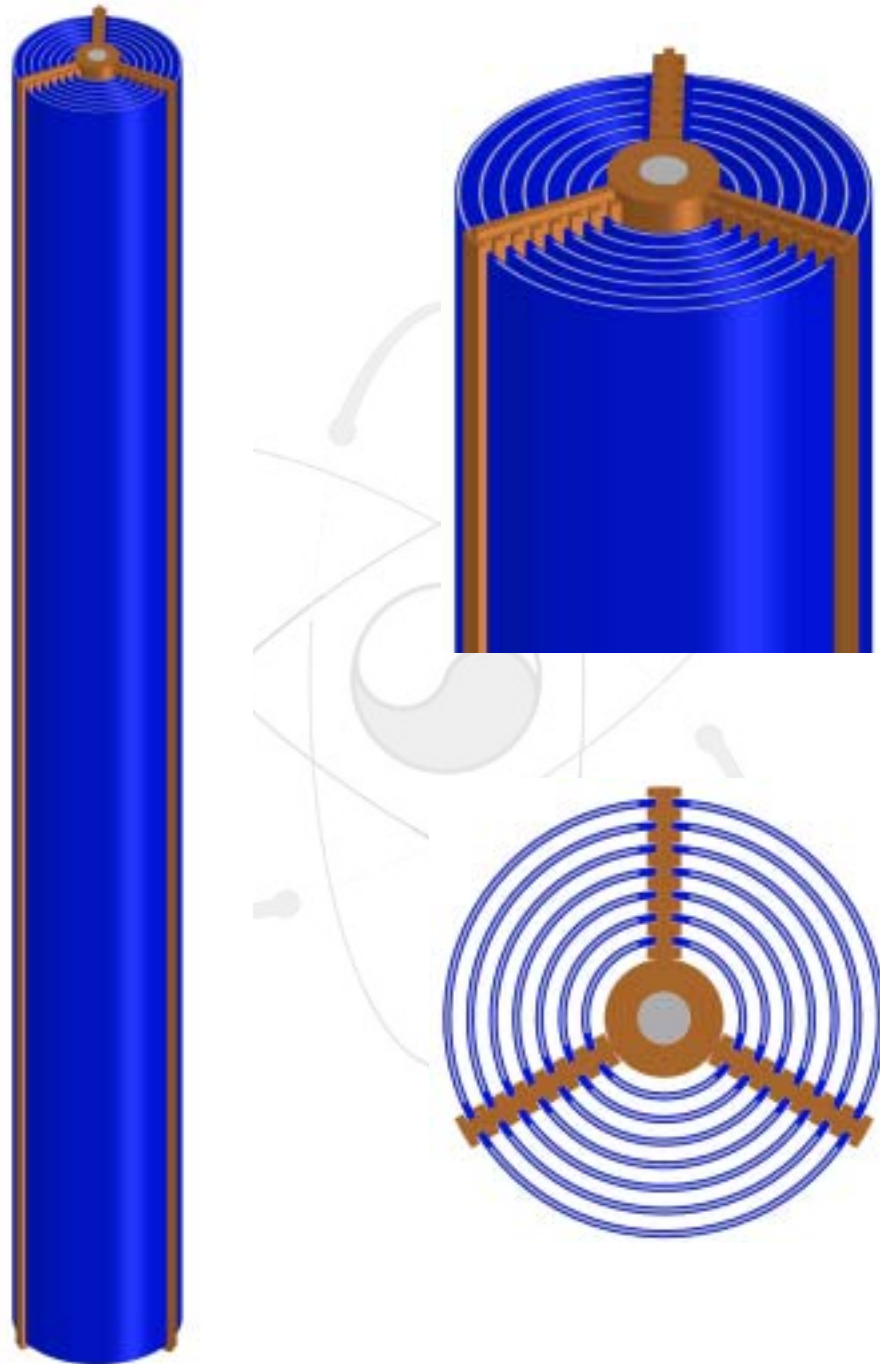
표준 핵연료집합체의 곡판 핵연료, stiffener, spacer tube 및 central rod의 조립도
